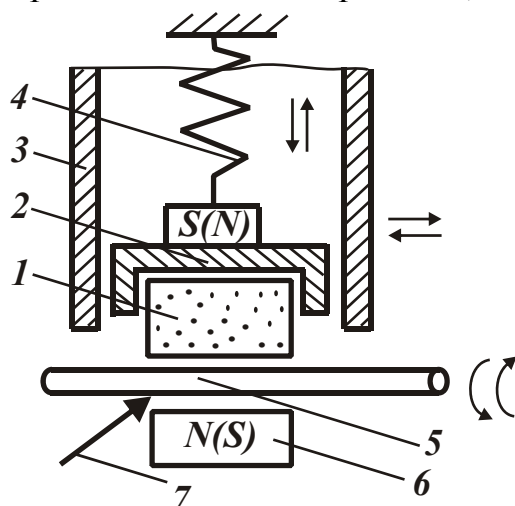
Схема магнито-импульсного шлифования: 1 – шлифовальный круг; 2 – патрон для шлифовального круга с электромагнитом; 3 – направляющий цилиндр, по которому перемещается патрон со шлифовальным кругом; 4 – пружина подвески патрона со шлифовальным кругом; 5 – обрабатываемая деталь; 6 – электромагнит; 7 – лазерный луч контроля размеров обрабатываемой детали.
